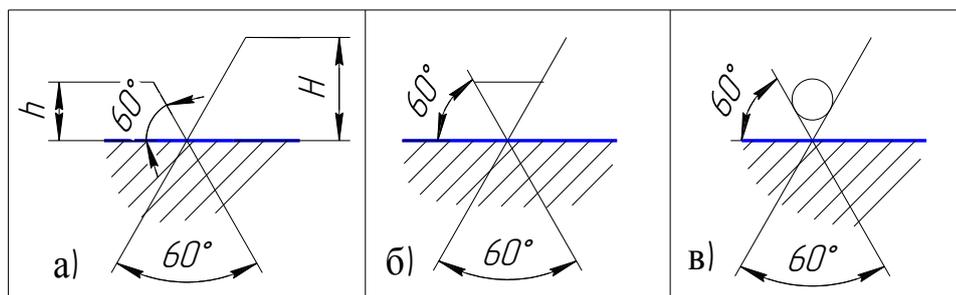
Знаки обозначения шероховатости поверхности [21]
